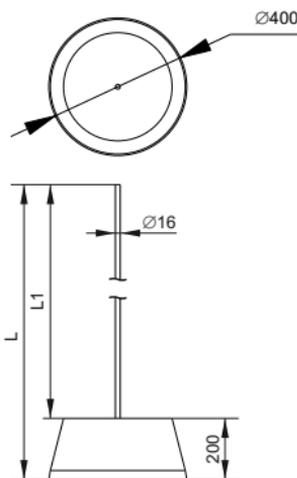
Габаритные размеры комплекта (1–3 м) / Figure 1 – Overall dimensions of the kit (1–3 m)
